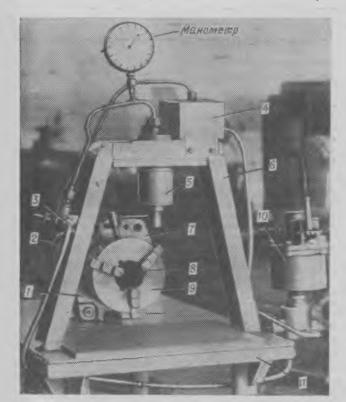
Стенд для разборки и сборки силовых карданных валов: 1— корпус: 2— роликовый подшипник; 3— трехходовой кран; 4— масляный бачок: 5— цильндр; 6— швеллер; 7— закрепляющее устройство; 8— металлическая труба; 9— токарный патрон; 10— автоматическая головка; 11— стол
